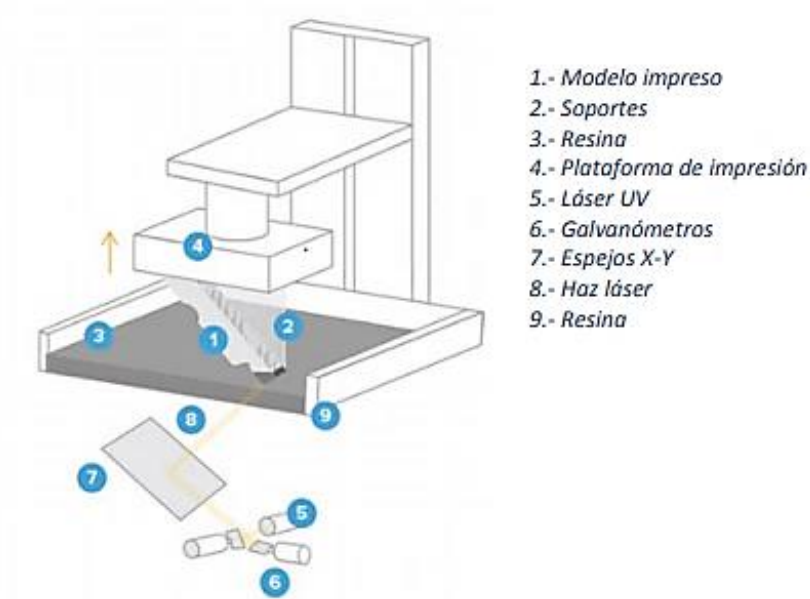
Partes constitutivas de una impresora 3D SLA. [15]
